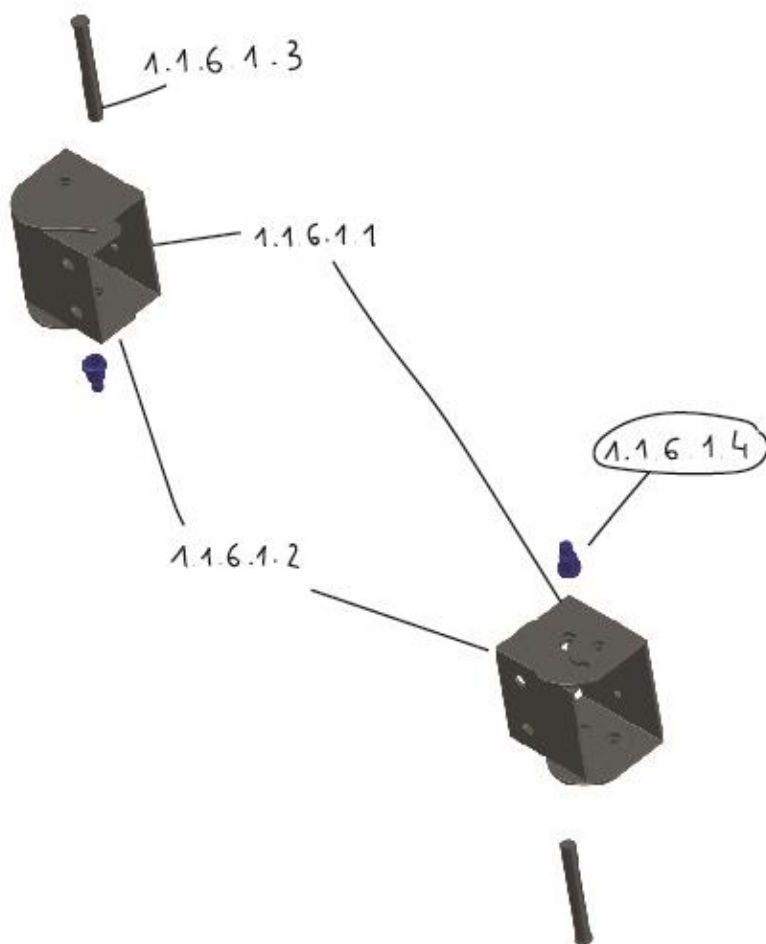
Explosionado de relaciones pieza 1.1.6.1.4
